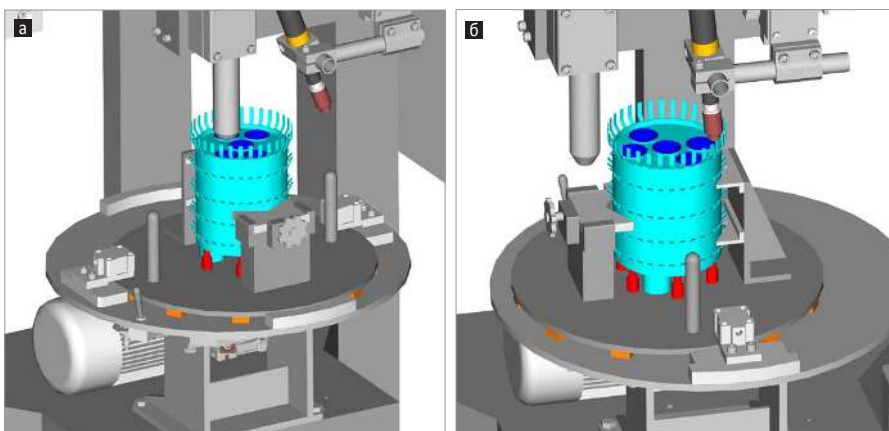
Схема работы установки АС399-С5, совмещение осей трубы и вращателя (а), сварка трубы (б)
